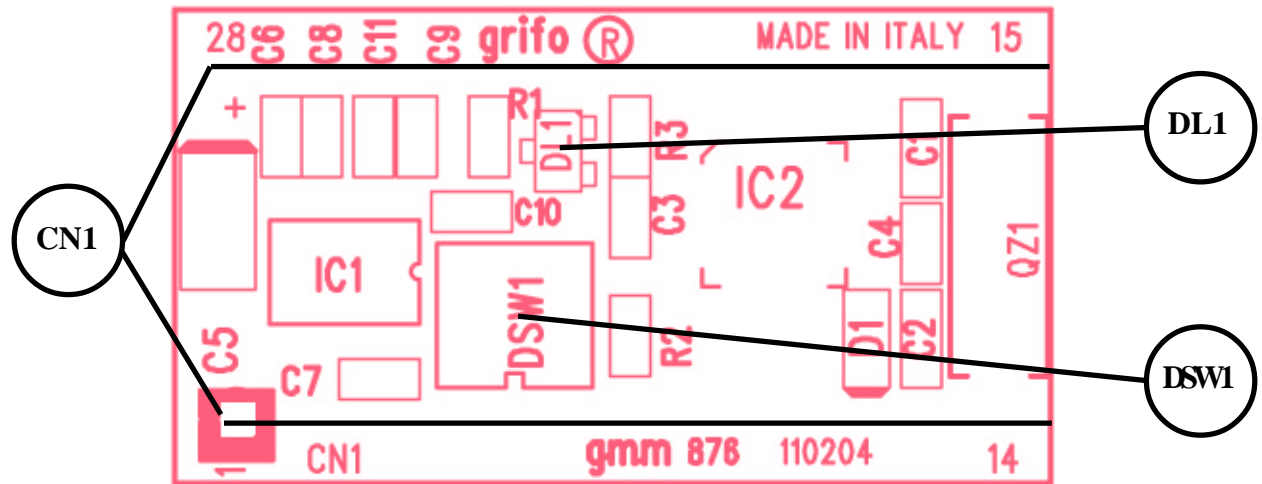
DISPOSIZIONE LED, DIP SWITCH, CONNETTORE, ECC.
